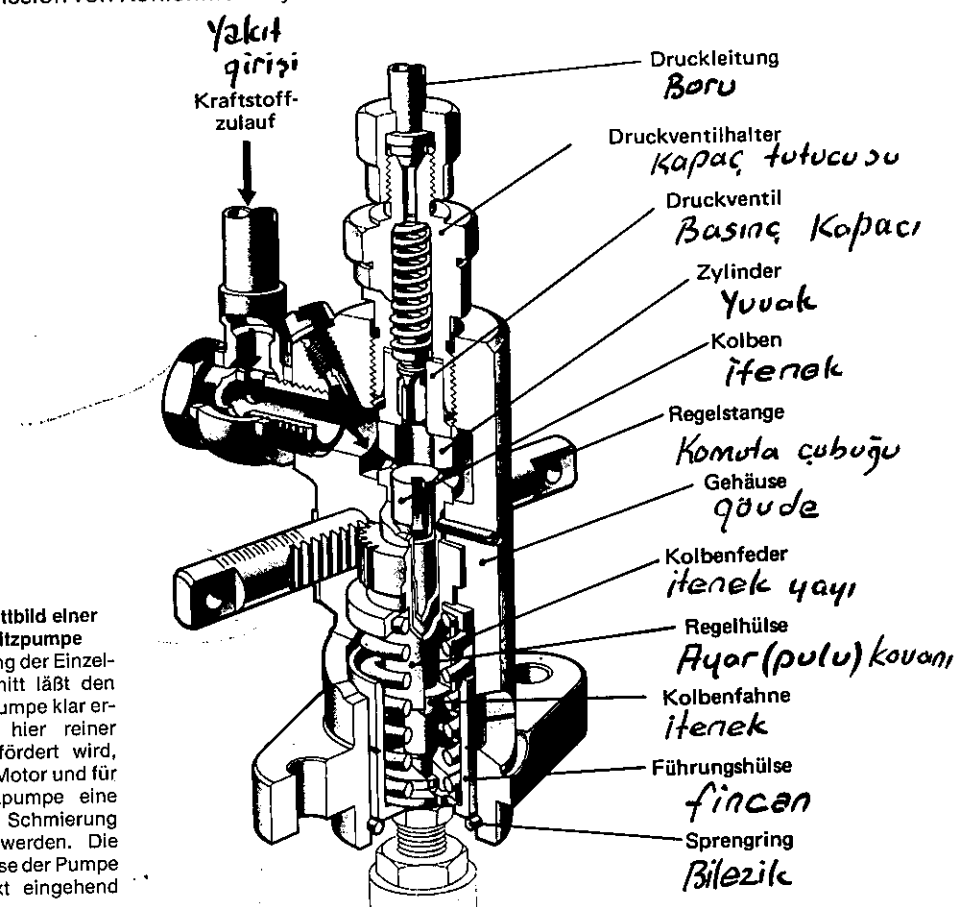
Schnittbild einer Bosch-Einspritzpumpe
